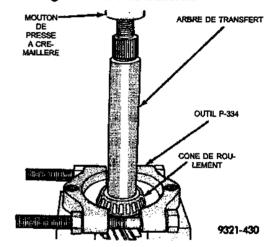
Dépose du cône de roulement d'arbre de transfert
